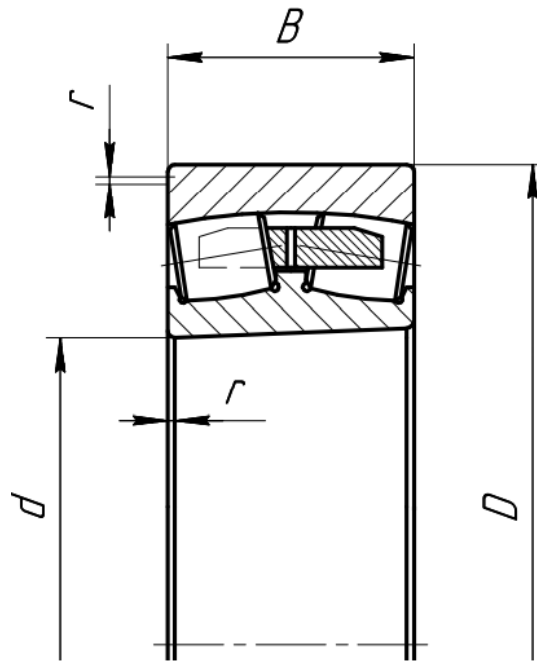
Підшипник роликовий сферичний дворядний
